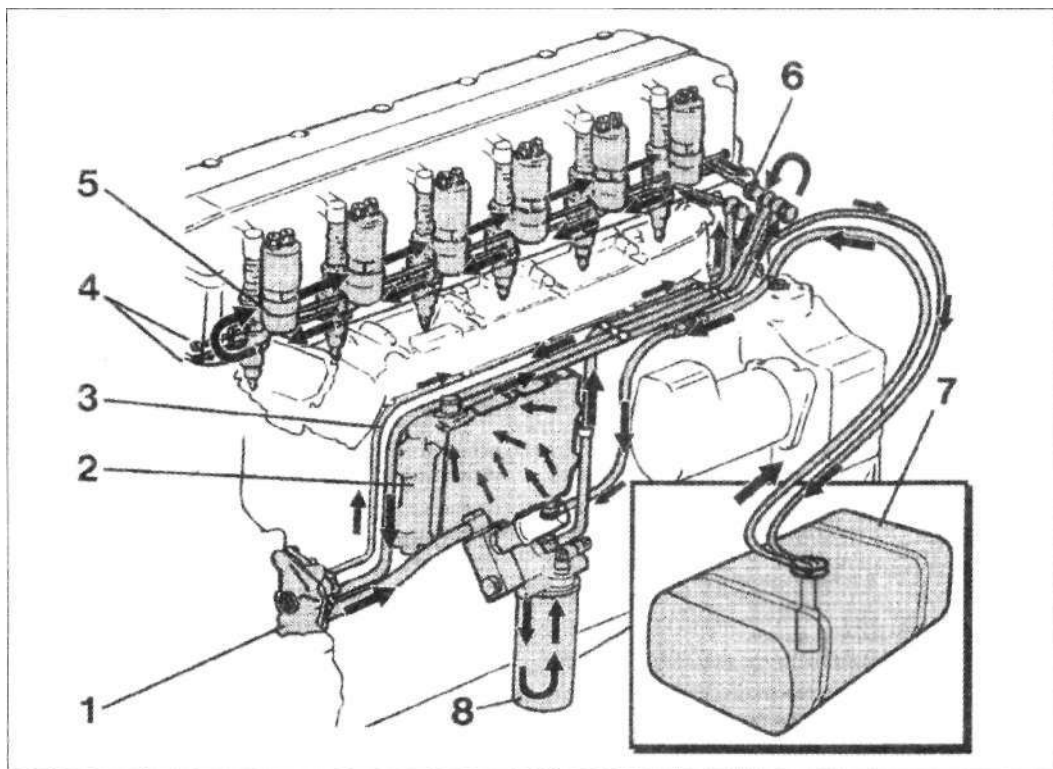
Устройство системы с насос-форсунками грузового автомобиля (источник: Volvo Trucks [13]): 1 — топливоподкачивающий насос; 2 — блок управления; 3 — трубопровод отвода воздуха; 4 — кольцевой канал; 5 — насос-форсунка; 6 — перепускной клапан; 7 — топливный бак; 8 — топливный фильтр тонкой очистки
